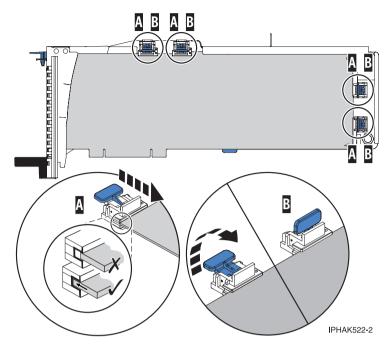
Langen PCIe-Adapter in PCIe-Adapterkassette installieren
